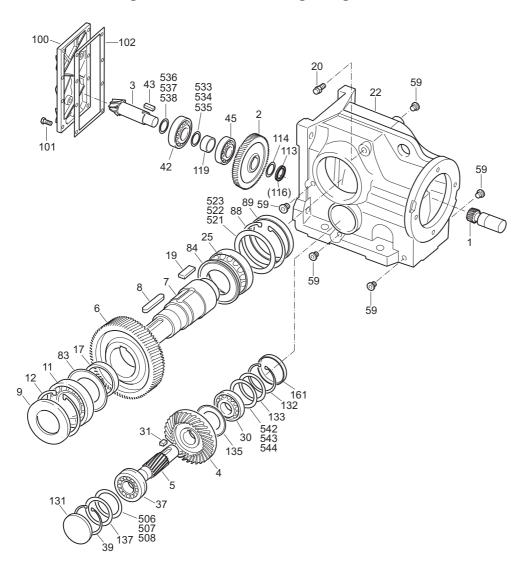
Estrutura geral do redutor de engrenagens cónicas
